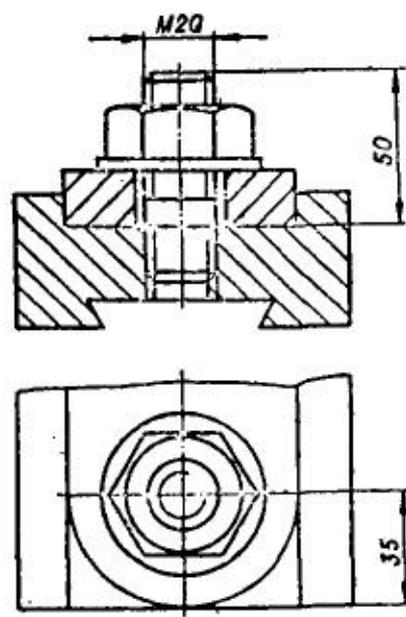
Конструктивне креслення шпилькового з'єднання.
